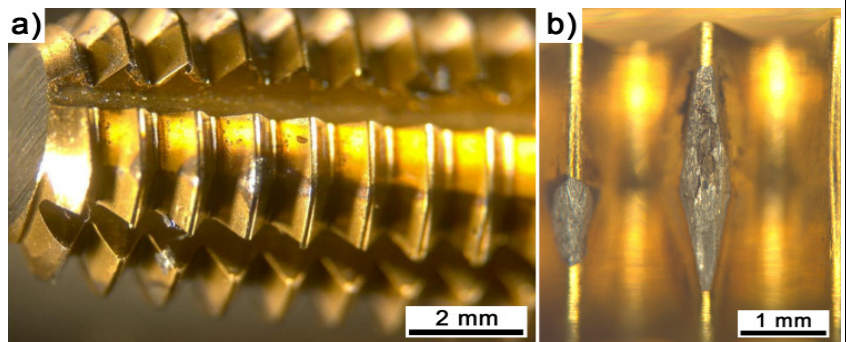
Makroaufnahme des Gewindeformwerkzeugs (a) Gesamtansicht eines mit Schädigung im Einlaufbereich; (b) Detail der Schädigung beim Erreichen des Werkzeugwechselkriteriums
